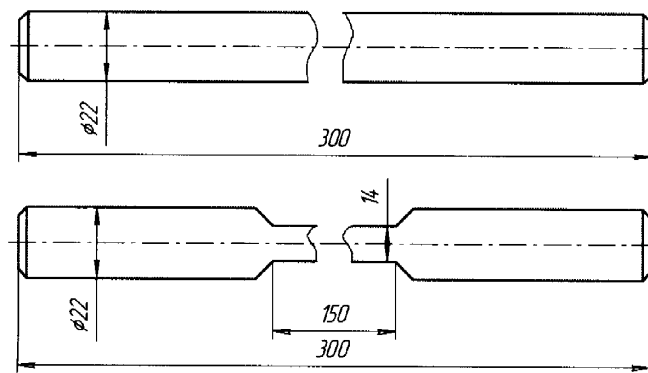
Ескізи зразків для випробування тіла склопластикової штанги на статичний розтяг
